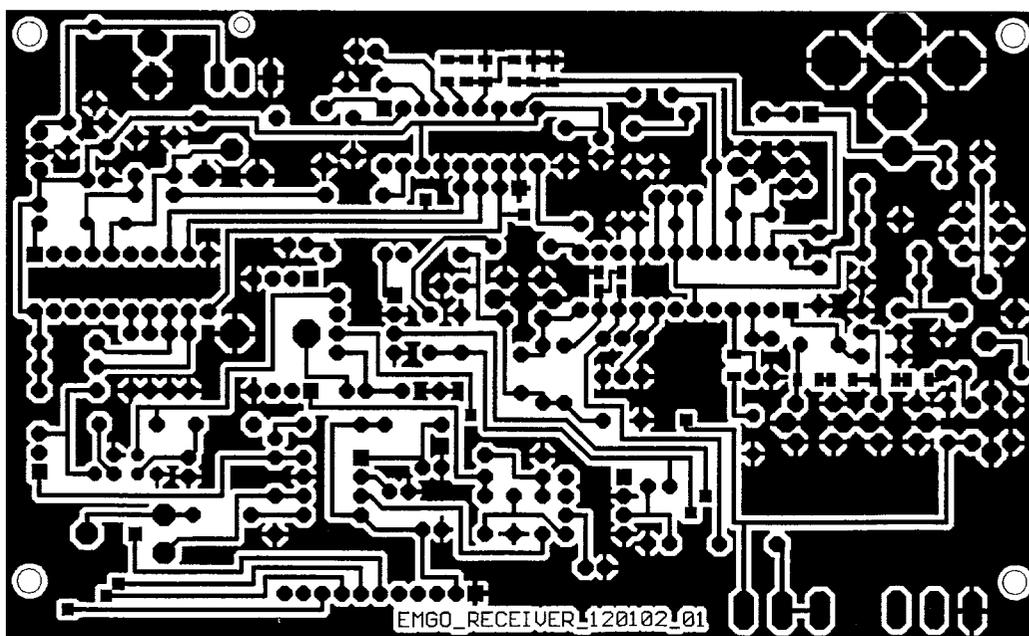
Le circuit imprimé de la carte mère du récepteur (côté soldures).
